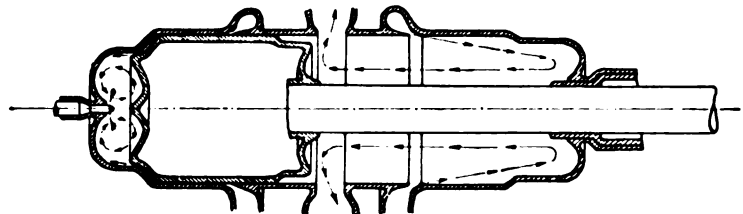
und 43. Doppeltwirkende Dieselmachine mit Schnellverbrennung
